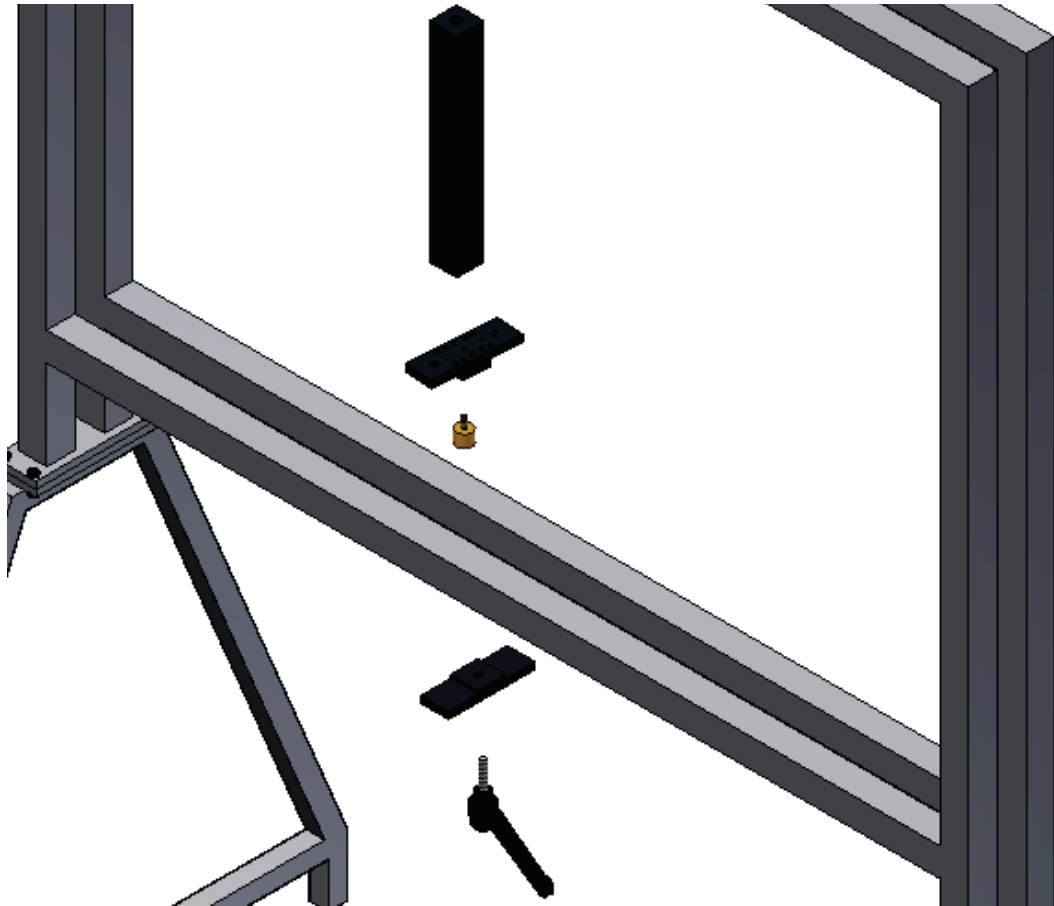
ensamble a detalle de los elementos de sujeción.
